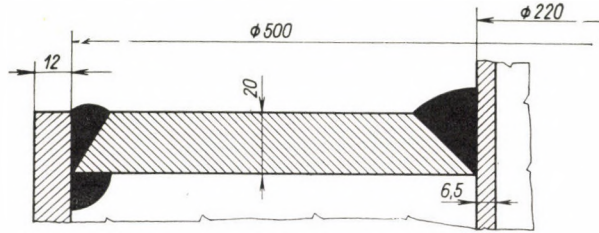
Abmessungen und Befestigung der Kreisringplatte. Ausführung der Schweißnähte
